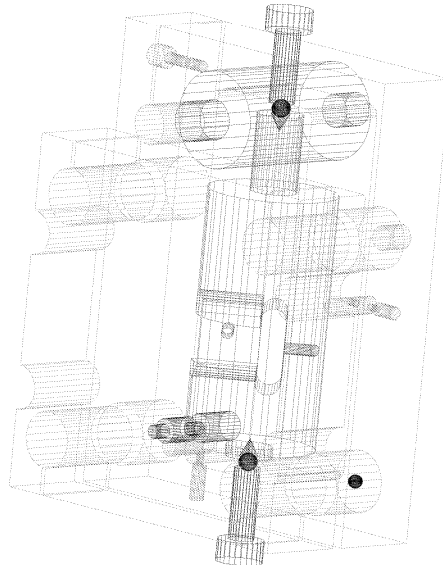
Vista frontal do desenho técnico do cabeçote posterior.
